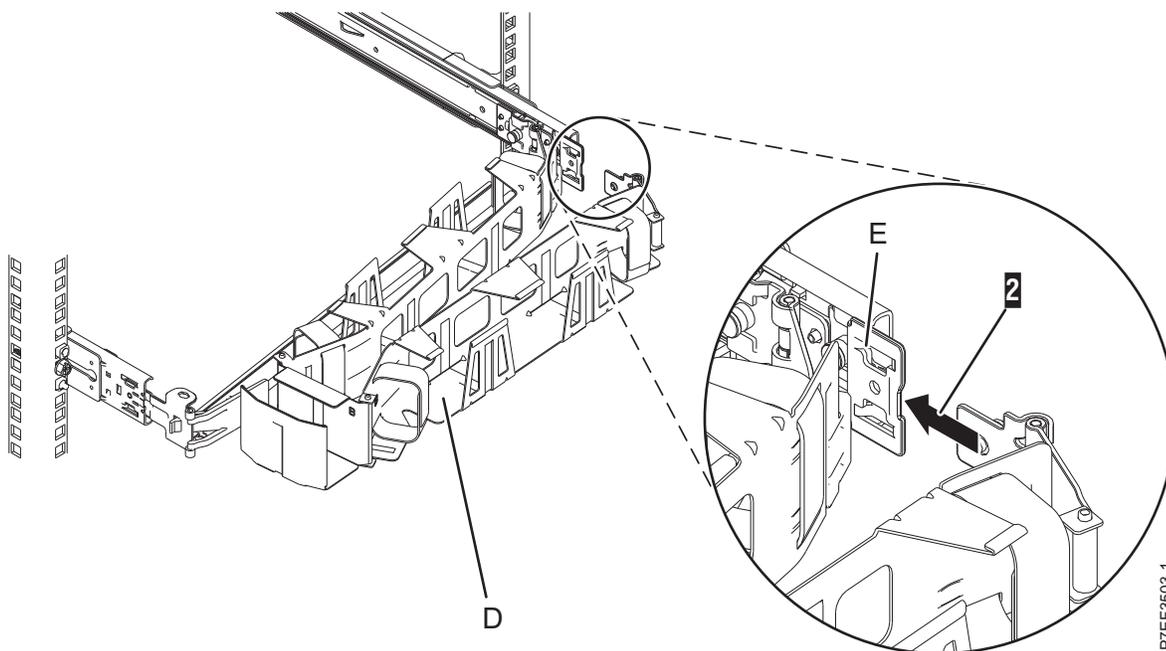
Faites glisser l'autre taquet du bras de routage des câbles dans le logement du support d'extension
